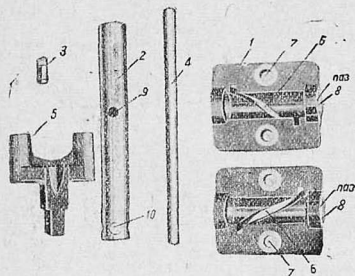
Детали приспособления для нарезки смазочных канавок. Справа показаны шаблоны приспособления
